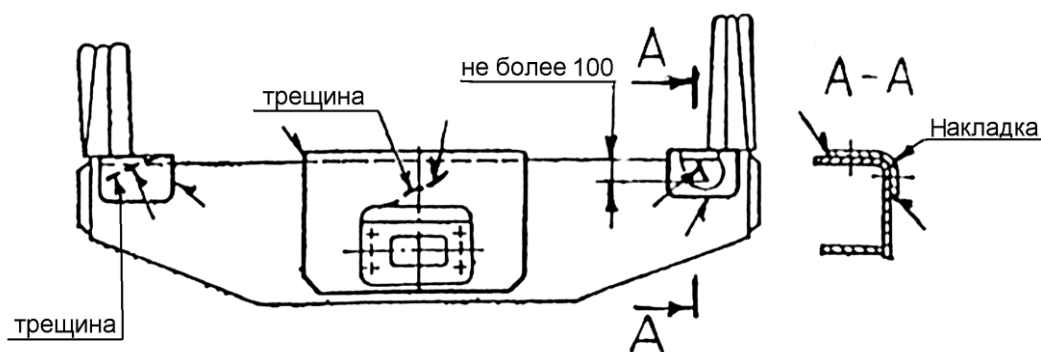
Балка полувагона с металлической обшивкой, отремонтированная сваркой
